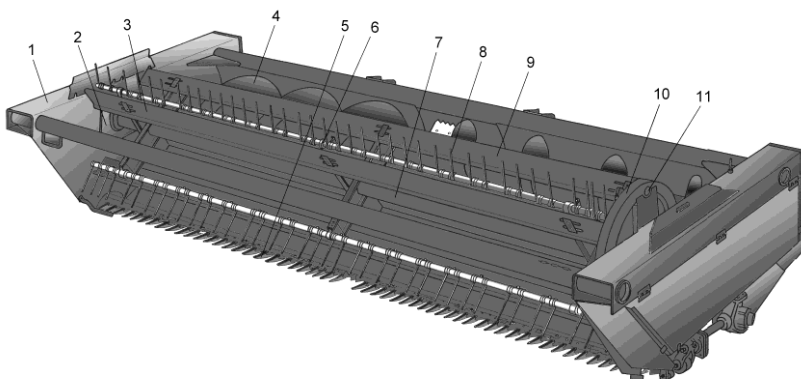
Жатка для трав: 1 – рама; 2 – опора мотовила; 3 – мотовило; 4 – шнек; 5 – режущий аппарат; 6 – граблина; 7 – вал мотовила; 8 – пружинный зуб; 9 – планка мотовила; 10 – направляющая дорожка; 11 – монтажное окно
